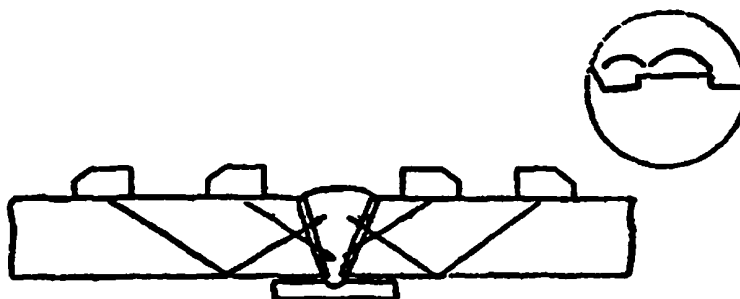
Схема контроля стыковых сварных соединений с подкладными пластинами;
